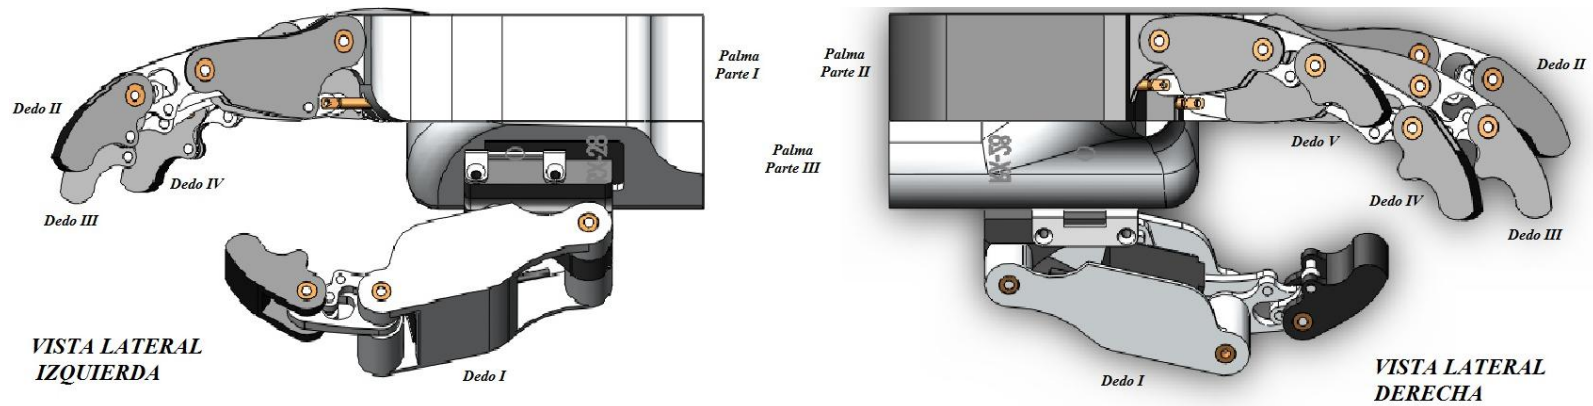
Prototipo de Mano Ensamblado en Vistas Laterales Izquierda y Derecha
